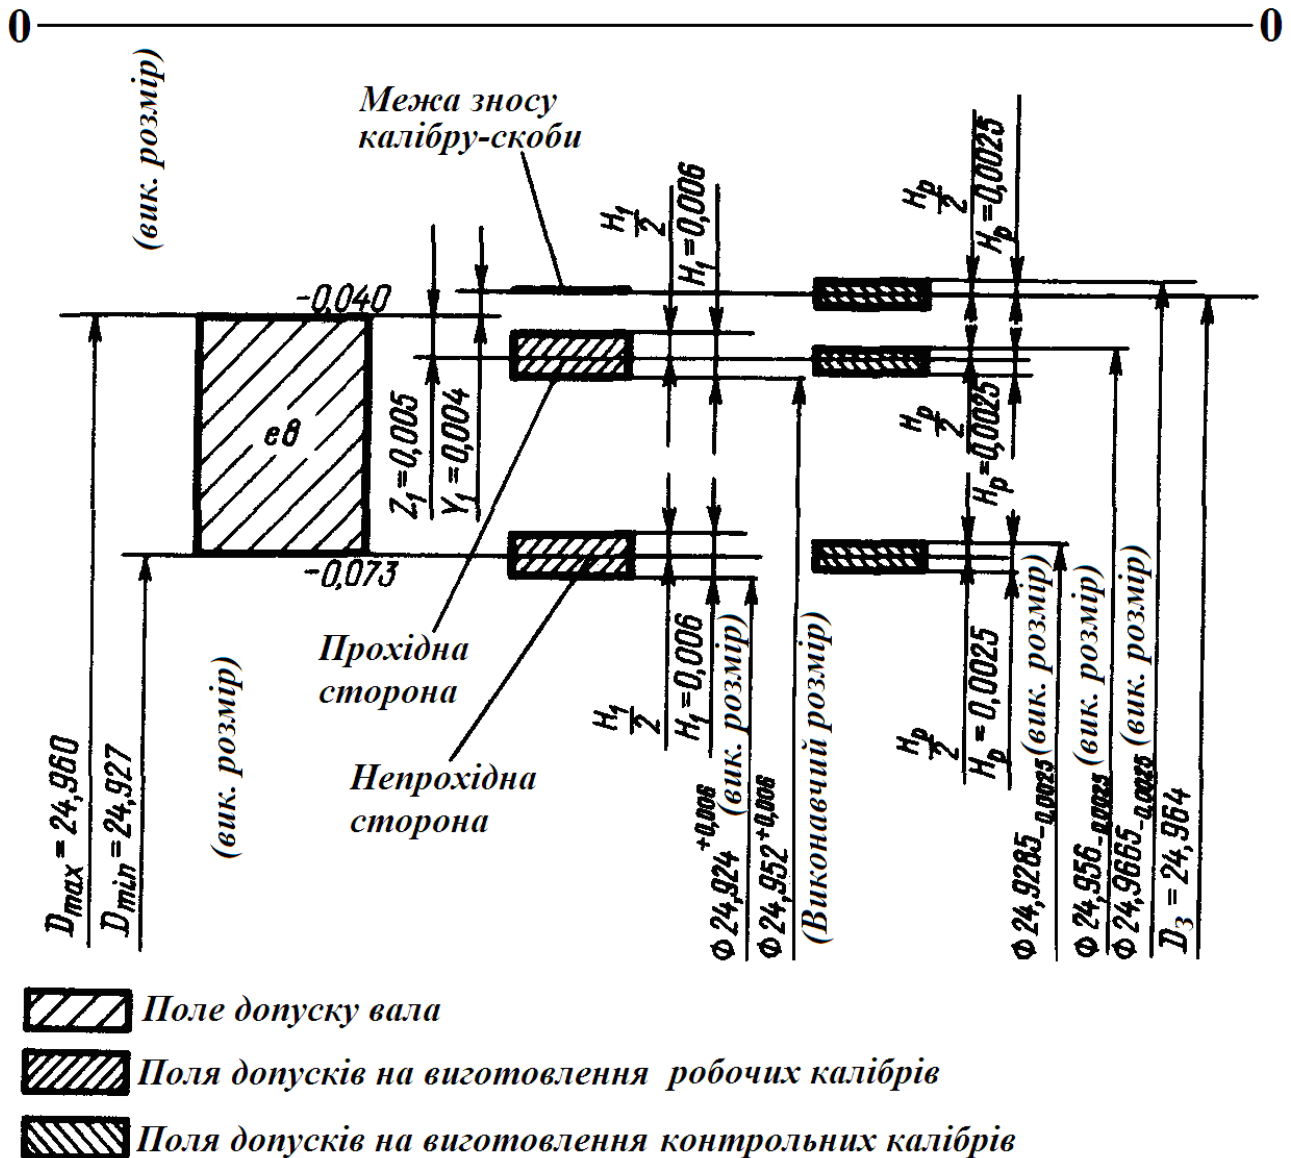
Схема полів допусків калібрів для контролю вала Ø25 e8
